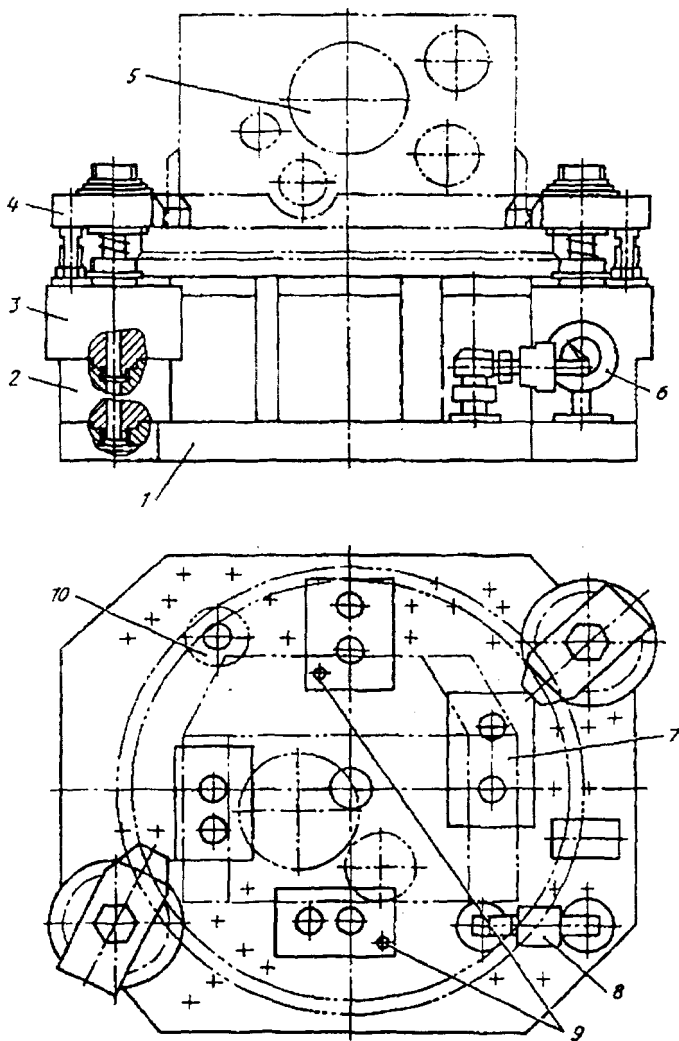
Механизированное приспособление для закрепления корпусных заготовок
